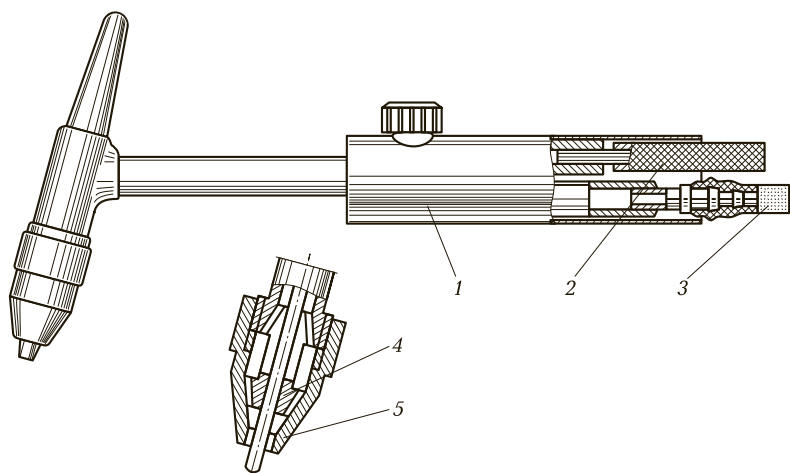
Горелка для аргодуговой сварки неплавящимся электродом:
